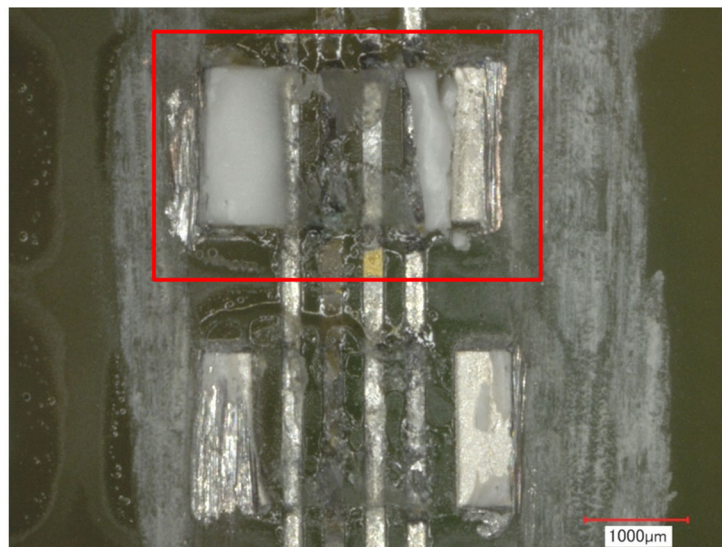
Testboard 133-1-1F-k nach Ablösung der Bauelemente R1206 (Detailansicht).
